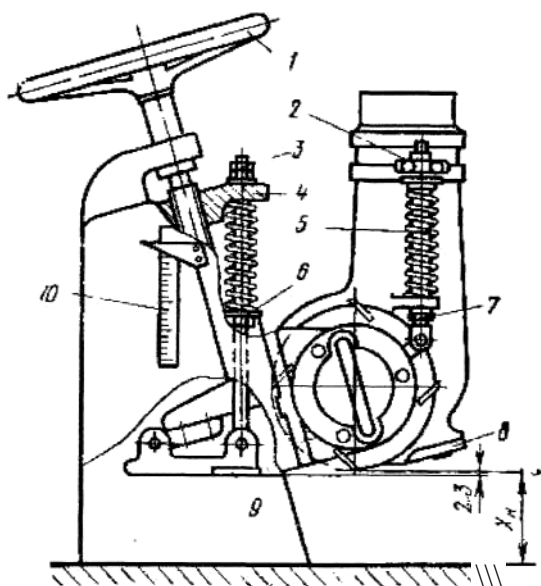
Настройка верхней горизонтальной ножевой головки четырехстороннего продольно-фрезерного станка.
